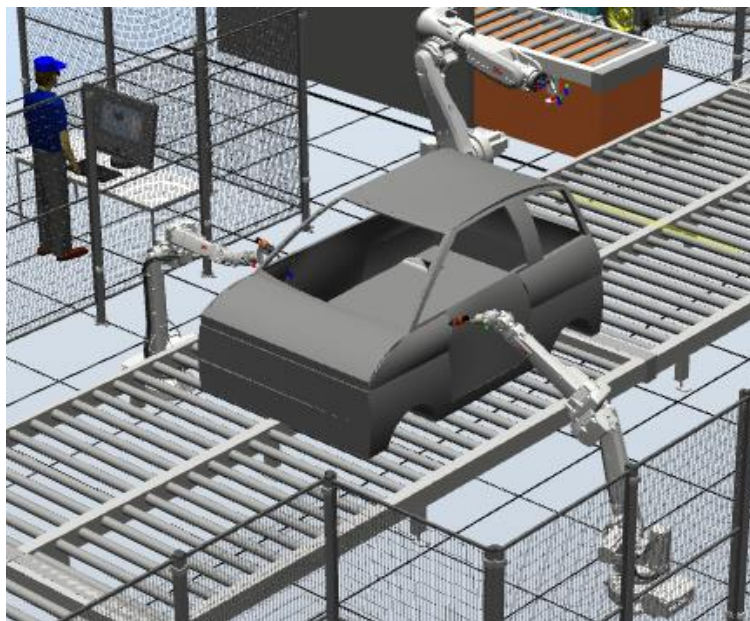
Soldadura de las piezas laterales por punto por resistencia.
